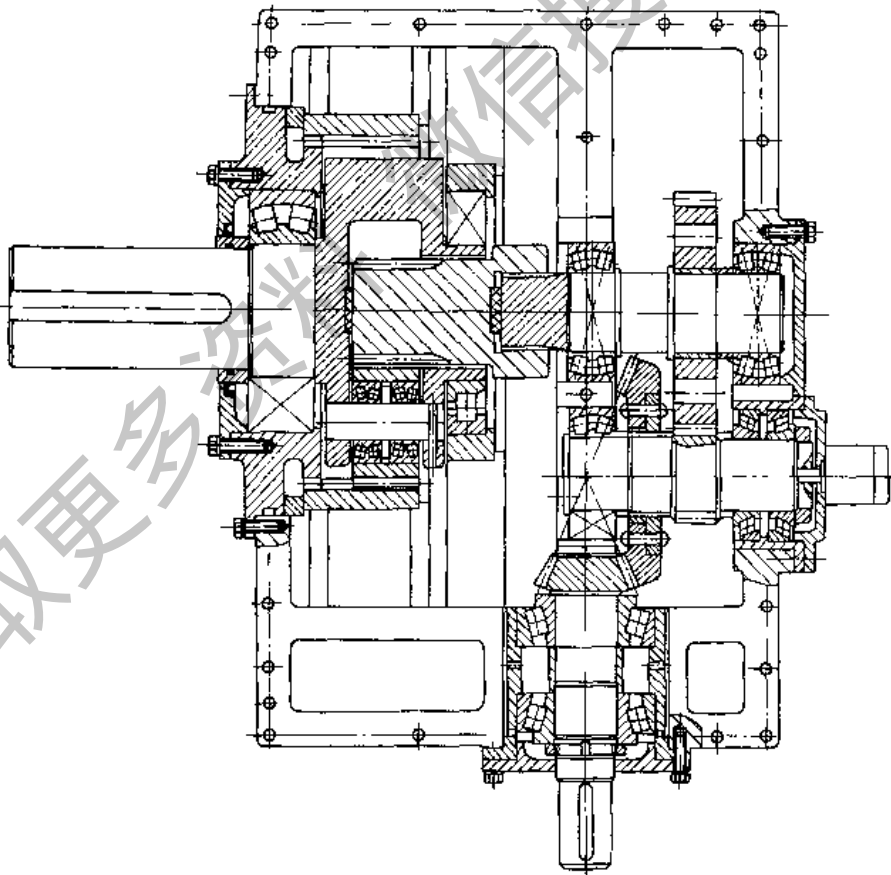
锥齿轮-柱齿轮二级减速器 (改进前)
